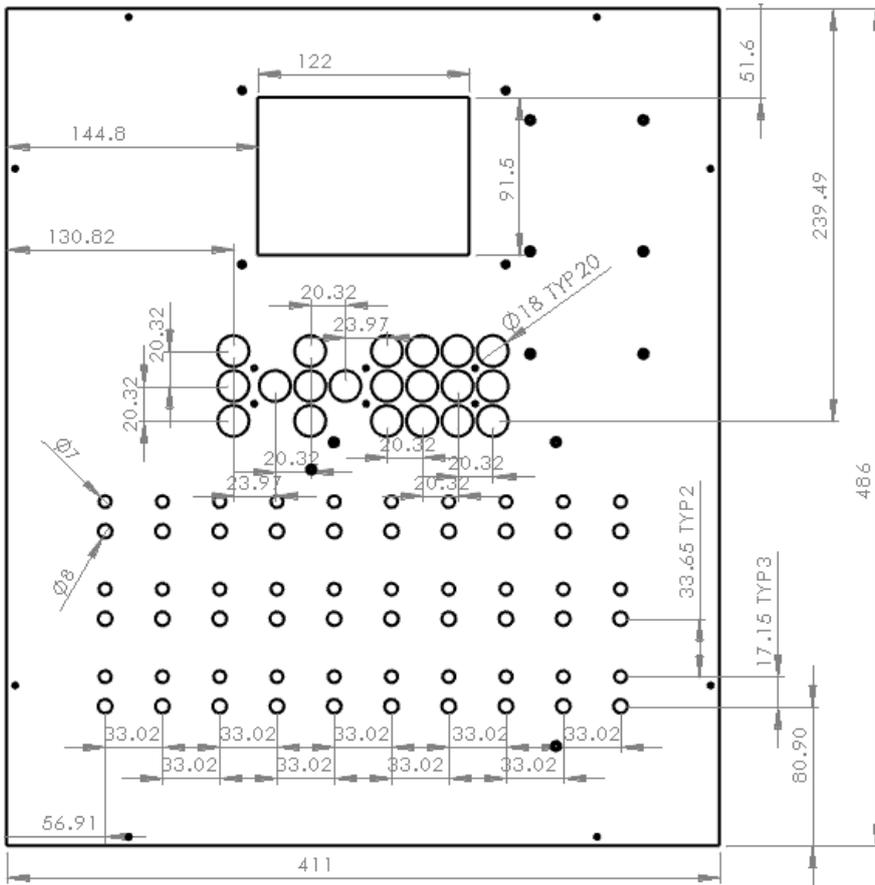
Platinum Pro 30 Dimensões do painel frontal
